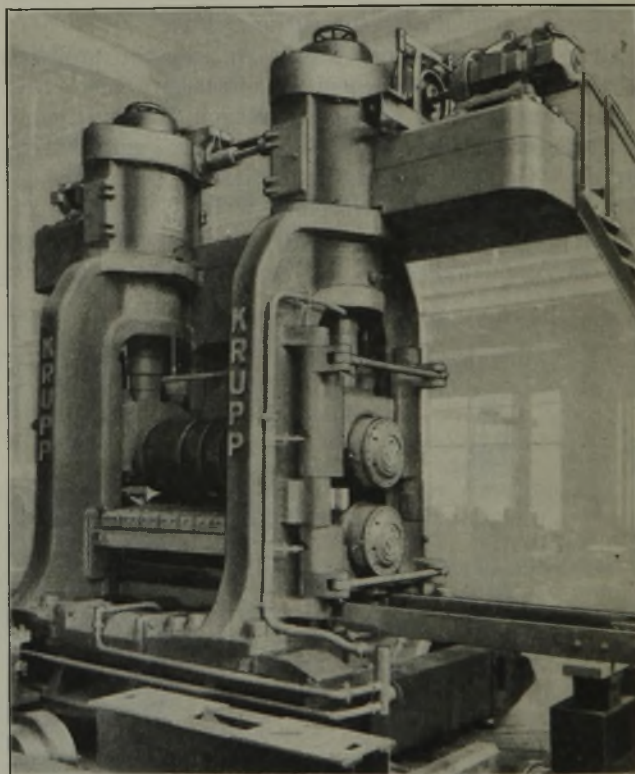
Zweiwalzen-Umkehrblockgerüst.
